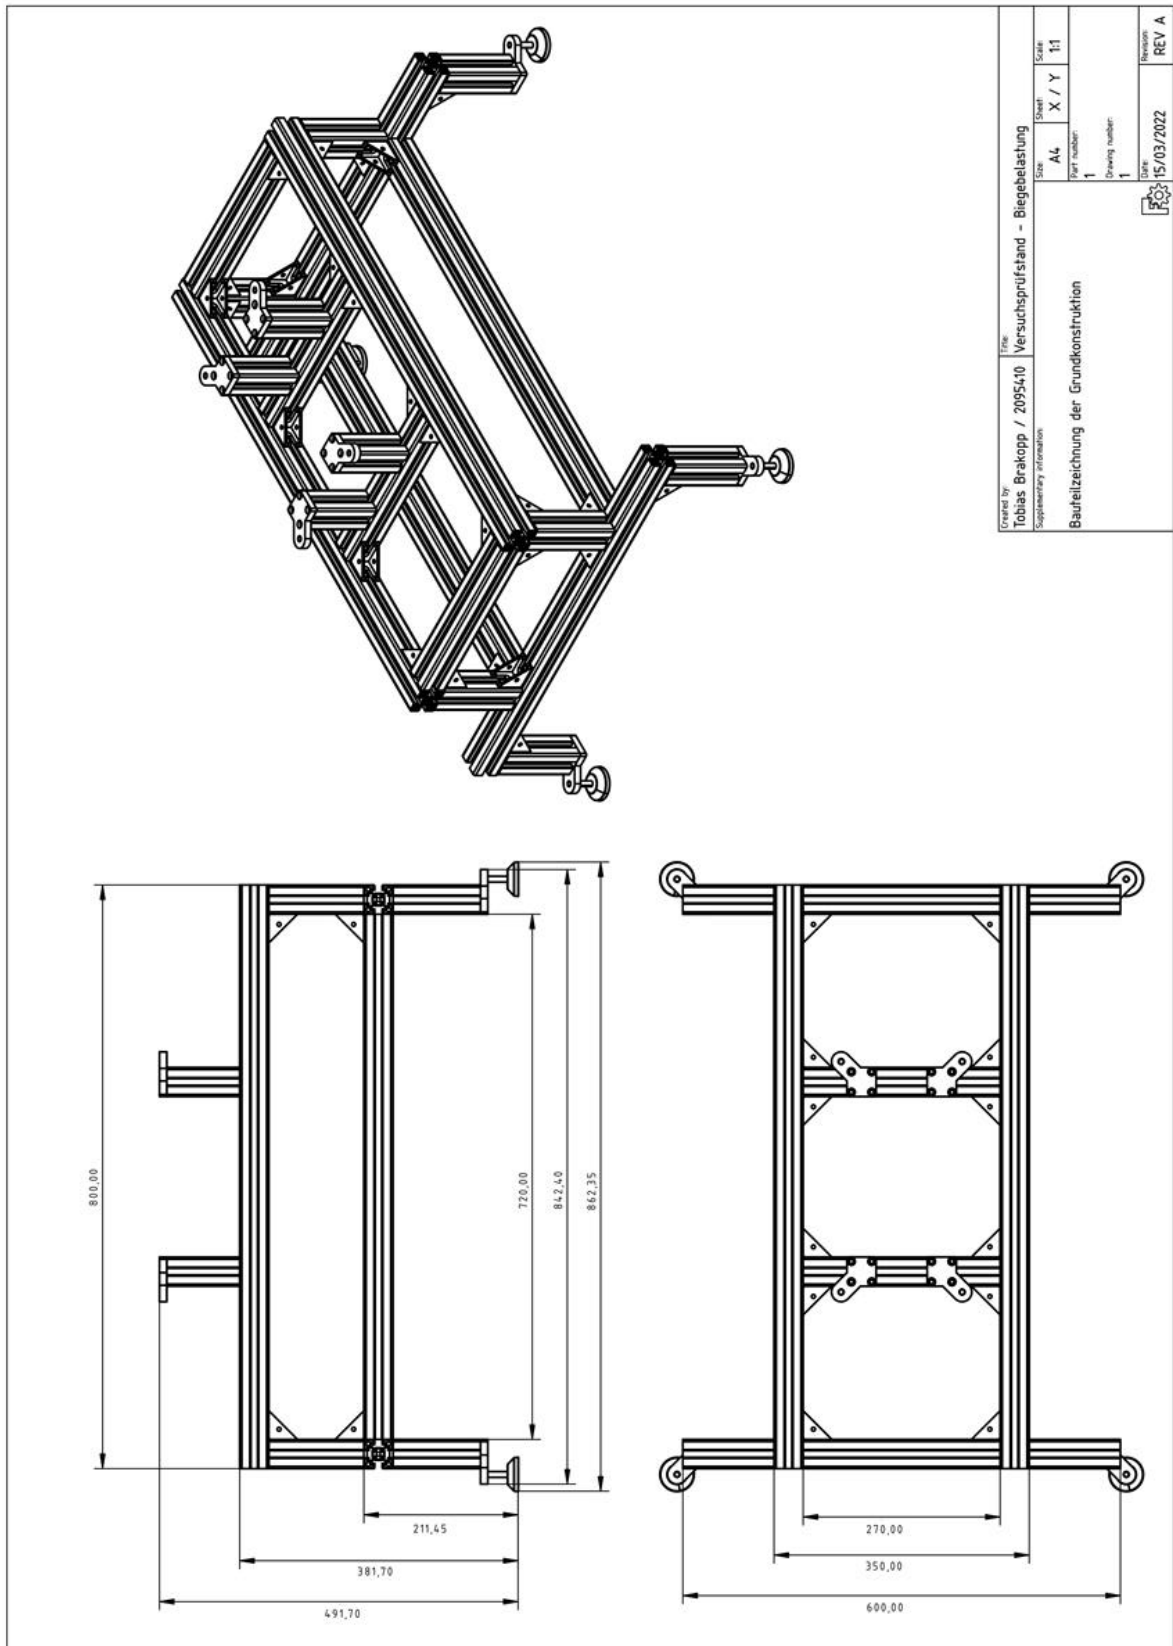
Technische Zeichnung - Versuchsprüfstand
